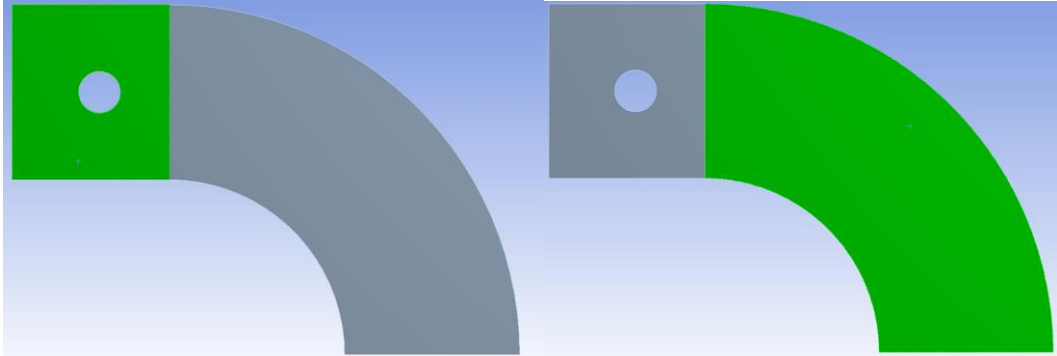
Superfície rectangular (esquerra) i superfície corba (dreta)
